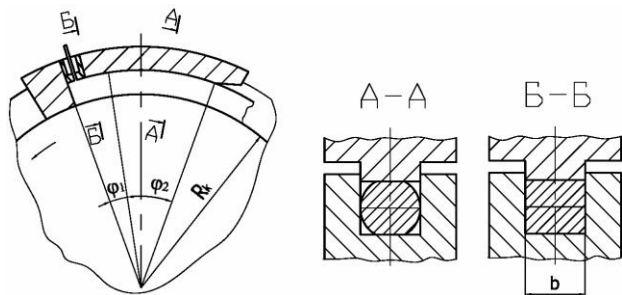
Зоны неполного (А-А) и полного (Б-Б) контакта заготовки с поверхностью контейнера
